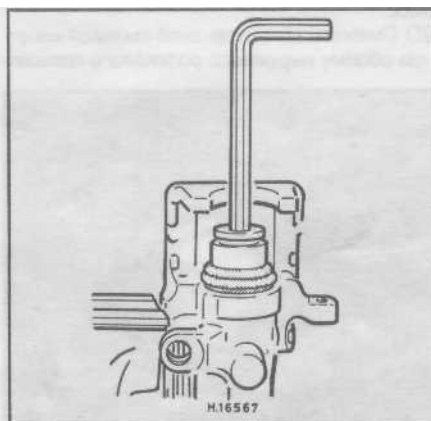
Вверните поршень в цилиндр сквозь защитный чехол
